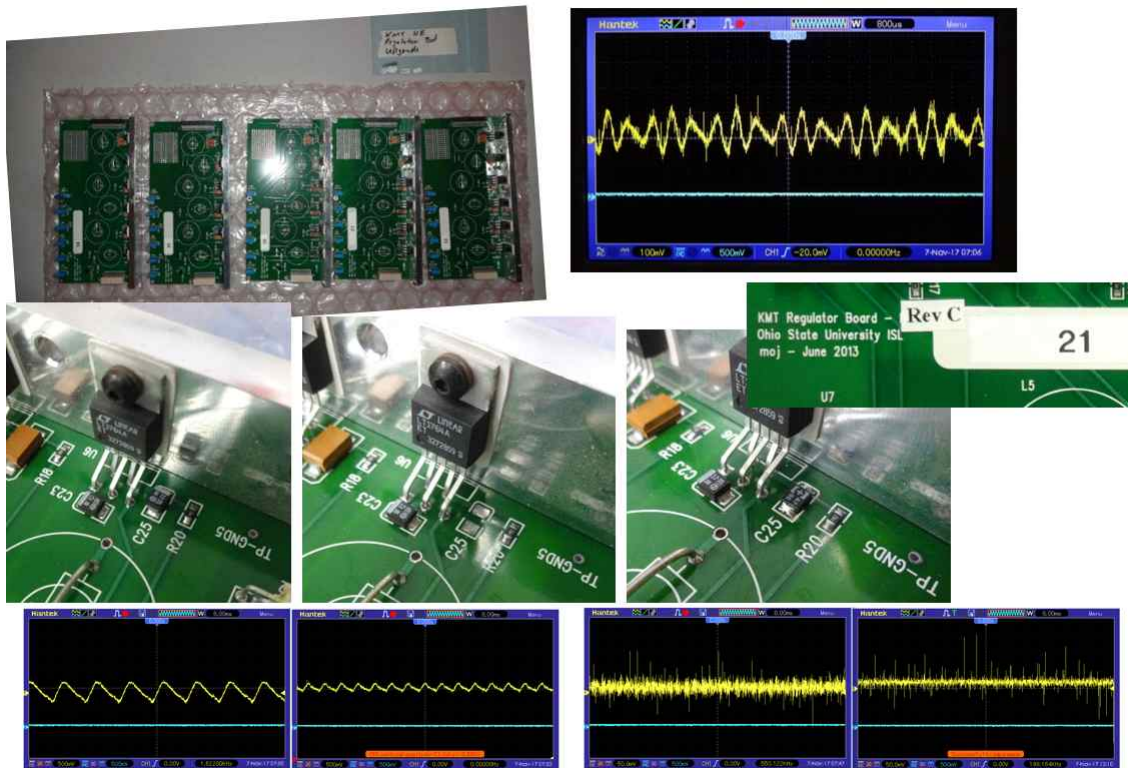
CCD 카메라 전자부의 Regulator board 부품교체 및 업그레이드
